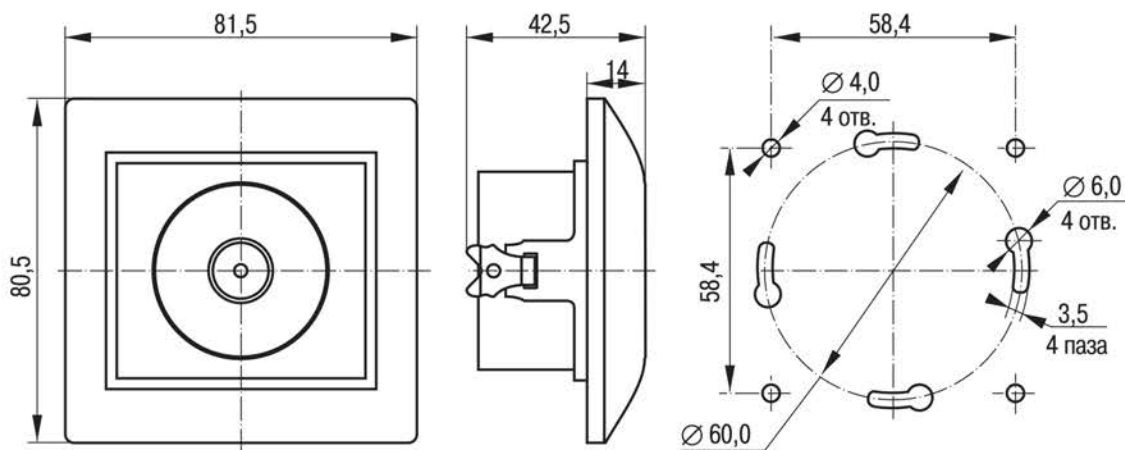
Габаритные и присоединительные размеры РТВ10-КБ, РТВ10-ККм
